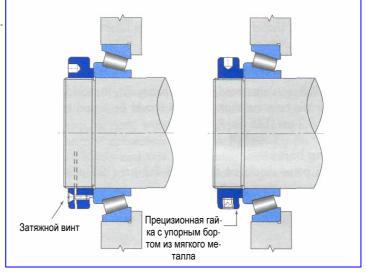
Приспособления для установки подшипников - X-сопряжение.
